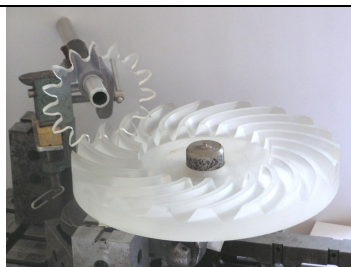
Прототип цилиндро-конической двухпараметрической зубчатой передачи
